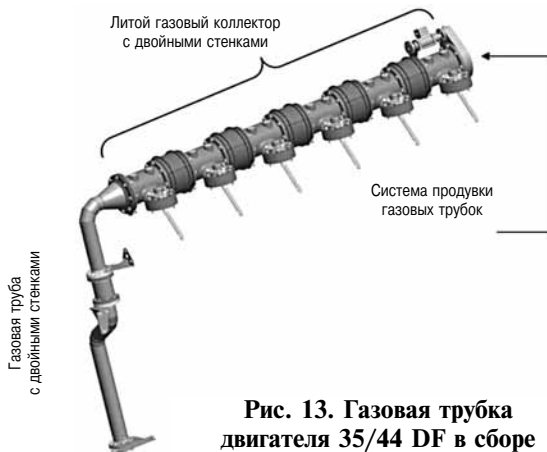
Газовая трубка двигателя 35/44 DF в сборе
